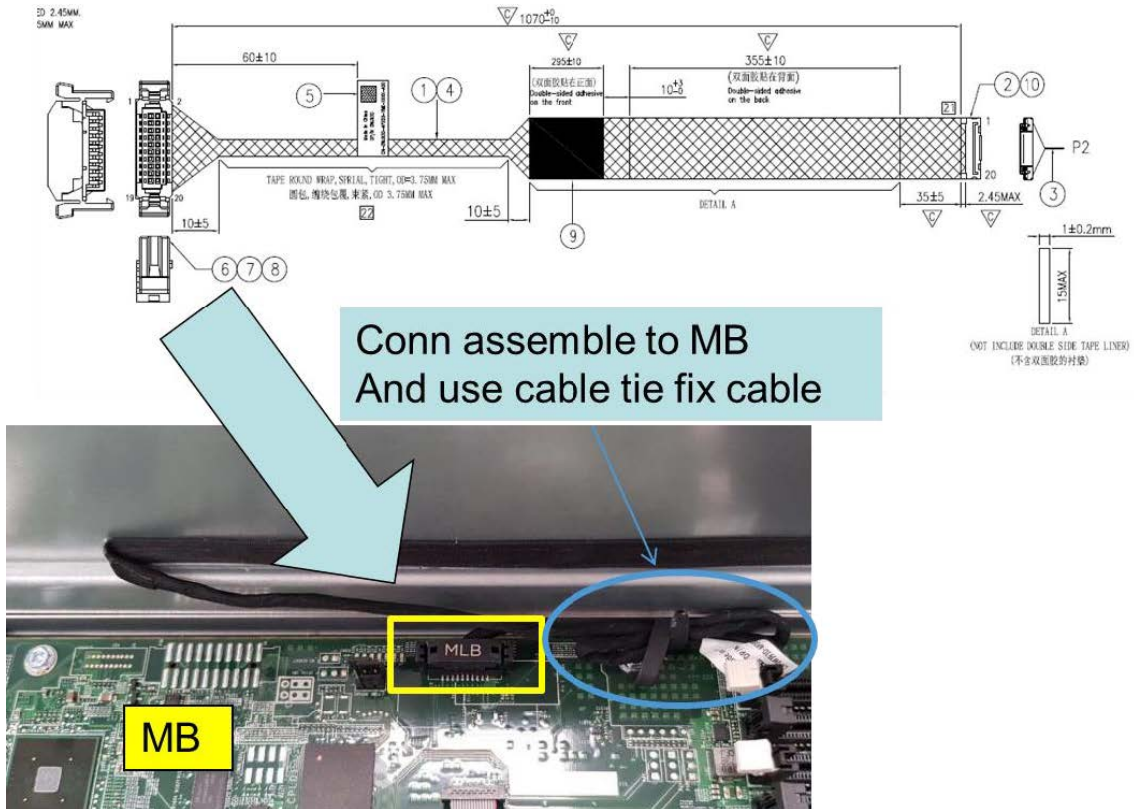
Panneau de commande et assemblage du câble de contrôle vers MB
